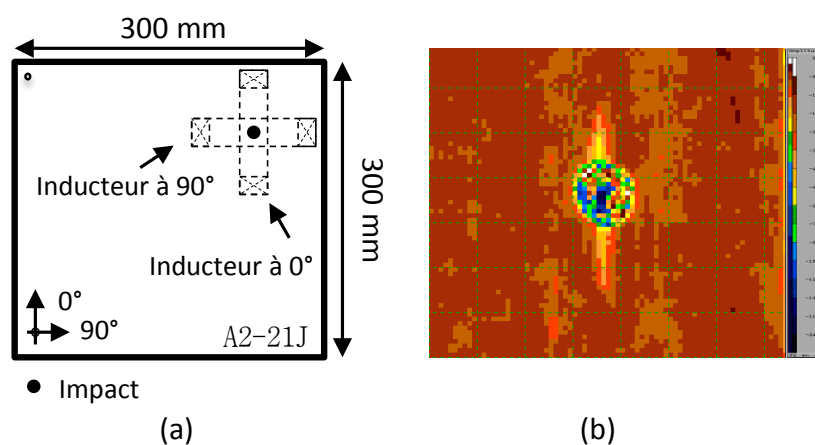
(a) La plaque composite avec un défaut d'impact, (b) L'image du défaut obtenue par la technique ultrasonore.
